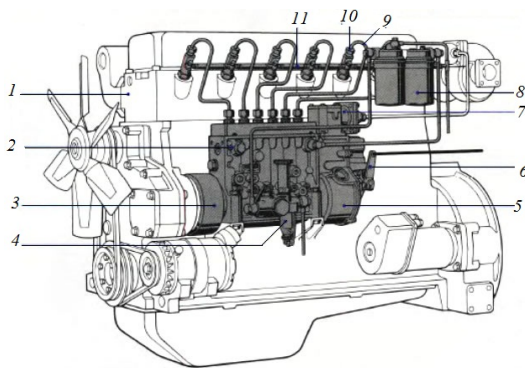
Схема питания дизеля: 1 – дизель; 2 – стандартный рядный ТНВД; 3 – муфта опережения впрыскивания; 4 – топливоподкачивающий насос; 5 – регулятор частоты вращения коленчатого вала; 6 – установочный рычаг с тягой от педали газа; 7 – ограничитель полной подачи, зависимый от давления наддува; 8 – фильтр тонкой очистки топлива; 9 – магистраль высокого давления; 10 – форсунка в сборе; 11 – магистраль обратного слива топлива
